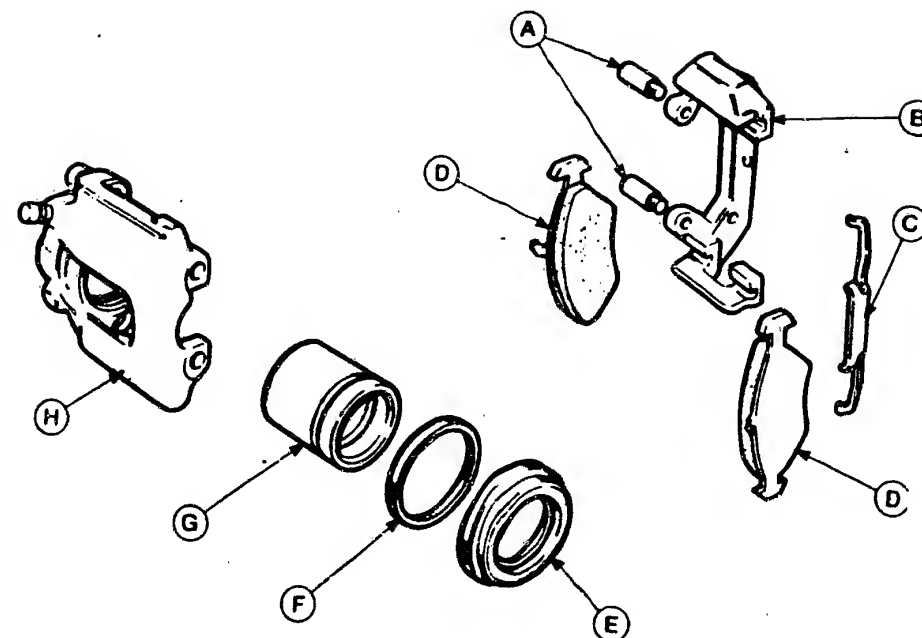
Schwimmersattel der 2,0-l- und der 2,3-l-Modelle: A Befestigungsschrauben – B Bremsklotzträger – C Halteklammer – D Bremsklötze – E Staubmanschette – F Kolbendichtung – G Kolben – H Kolbengehäuse.
